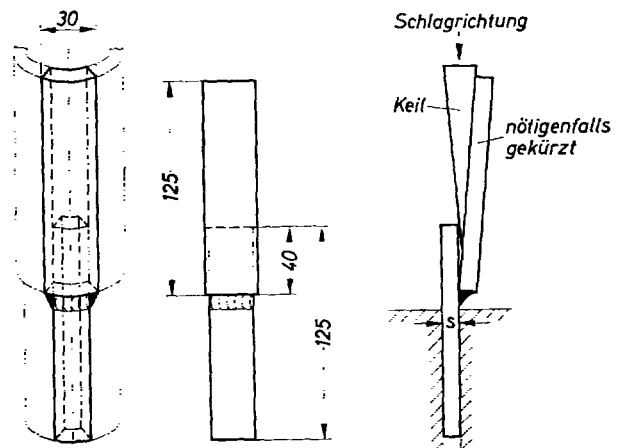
Rohr-Keilprobe für Kehlnähte am Überlappstoß für Rohrschweißer an $s \geq 4$ mm (Prüfstück entsprechend Bild 14)
